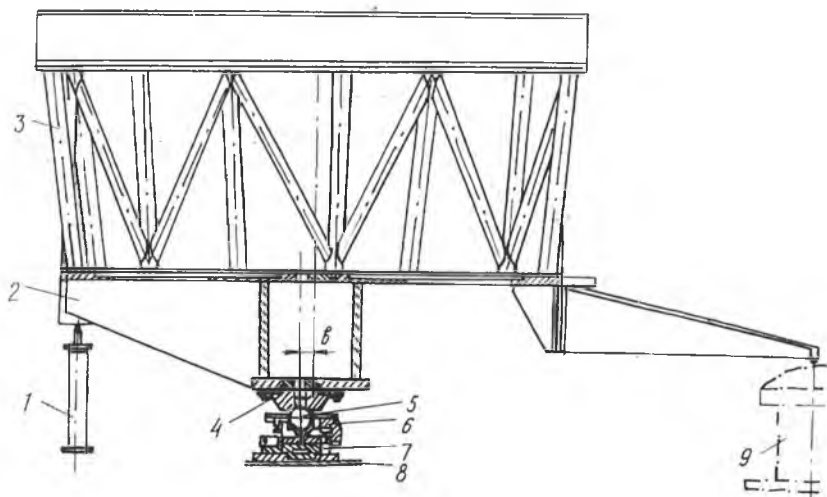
Стент статической балансировки с гидроопорой и двумя пневмодатчиками
